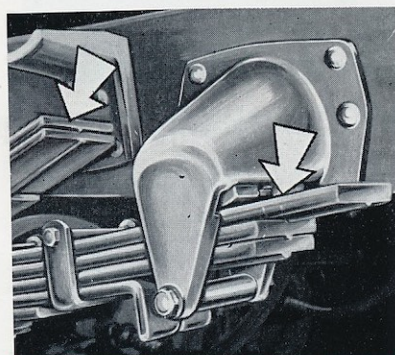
Graissage des mains arrière de ressorts arrière et patins de ressorts arrière.
